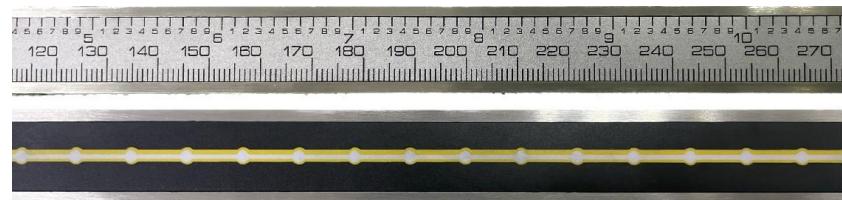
Общий вид штанг штангенциркулей с цифровым отсчетным устройством
